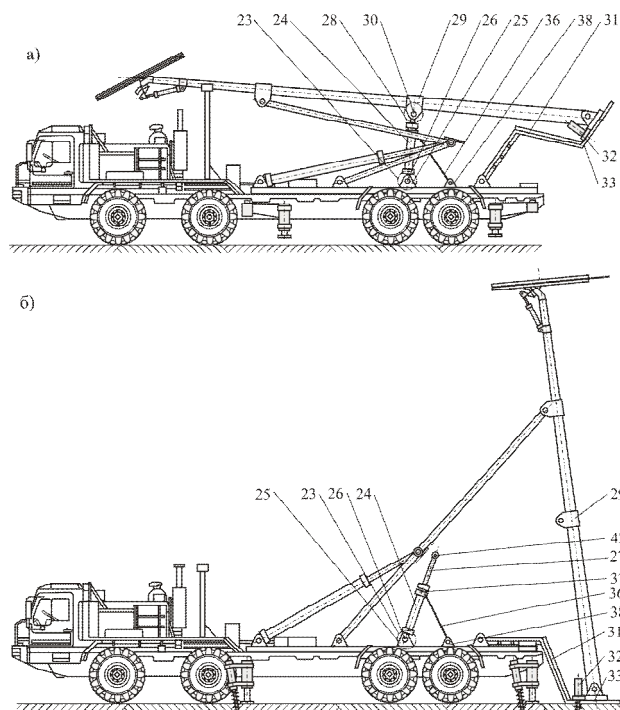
Общий вид самоходной машины (вид сбоку) с выносным расположением концевой опоры и складывающейся штангой (модификации Ву1-4/Х и Ву2-4/Х): а – транспортное положение концевой опоры; б – рабочее положение концевой опоры
